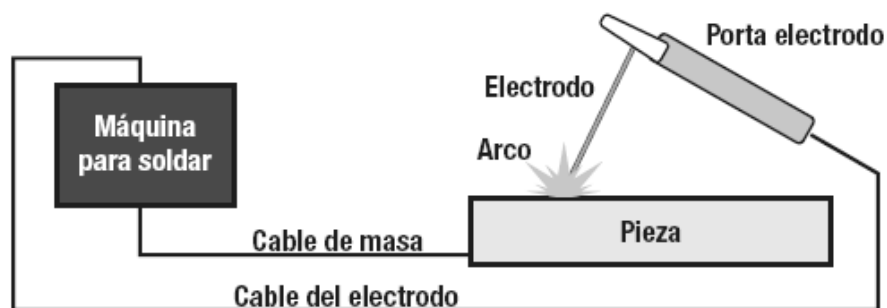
Esquema general del método de soldadura por arco eléctrico.
